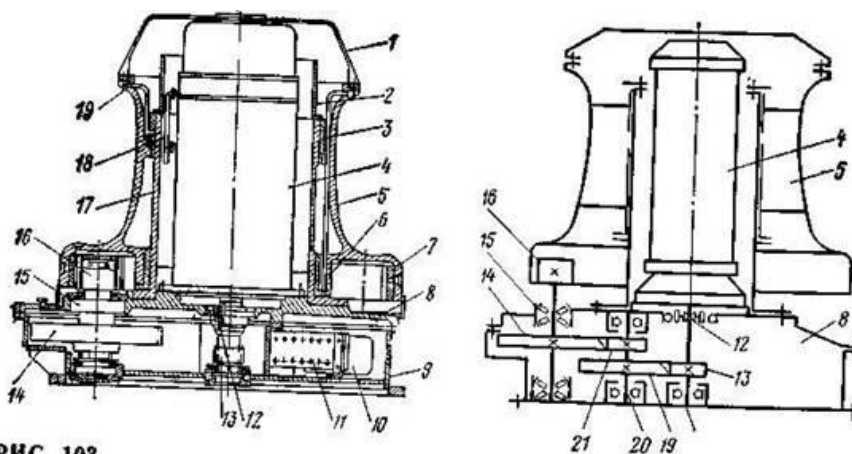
Кинематическая схема и общий вид шпиля типа Ш5
